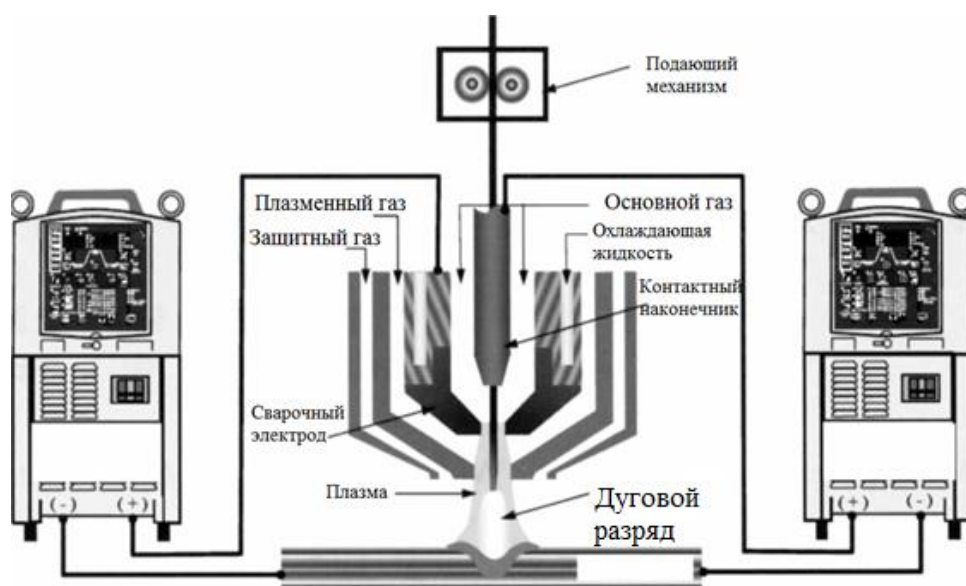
Схема плазменной сварки плавящимся электродом
